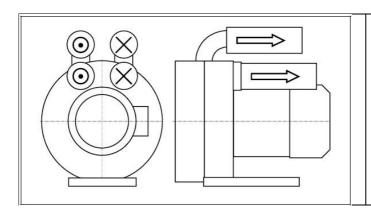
Двухпоточная конструкция вакуумного насоса/компрессора с двумя рабочими колесами.
